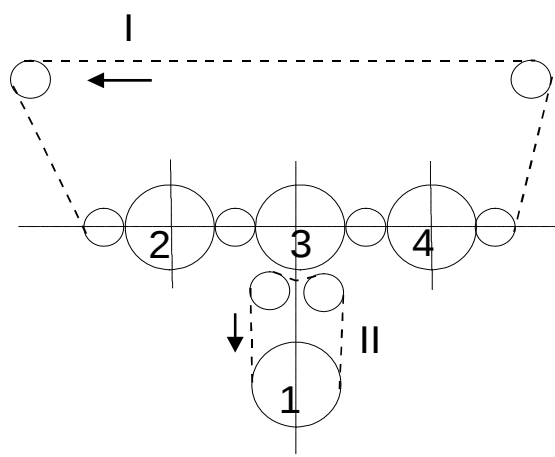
Схема линии сборки воспламенителей: 1 — загрузочный ротор; 2 — загрузочный ротор; 3 — ротор сборки двух элементов; 4 — контрольный ротор
